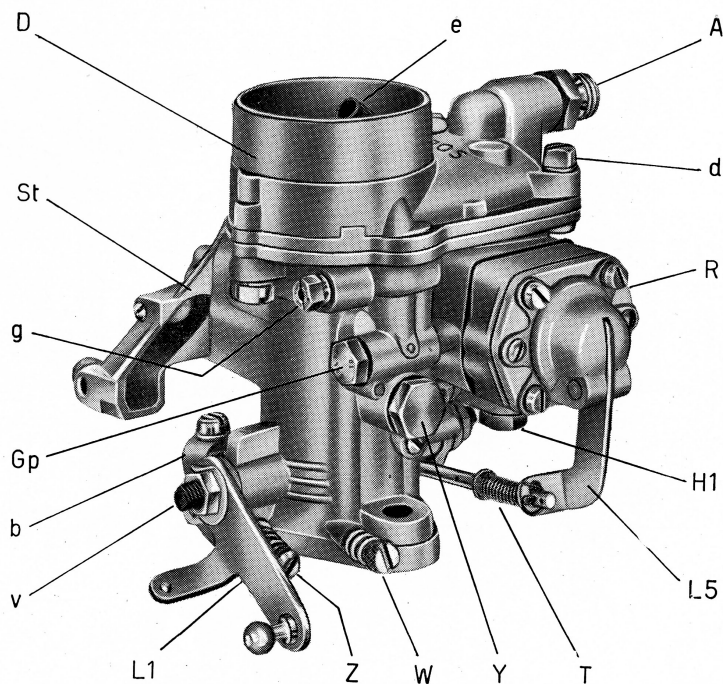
SOLEX-Vergaser Type 32 PICB – Ansicht
